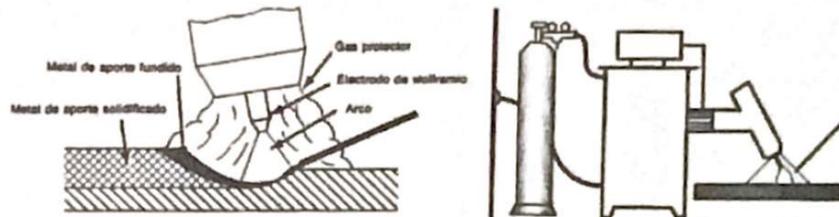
Soldadura TIG: Esquema del proceso y elementos del equipo de solda [DEG-1].
